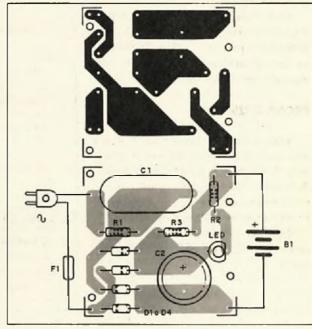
Montagem do carregador na placa (redimensionador a posição de C1 se necessário).
